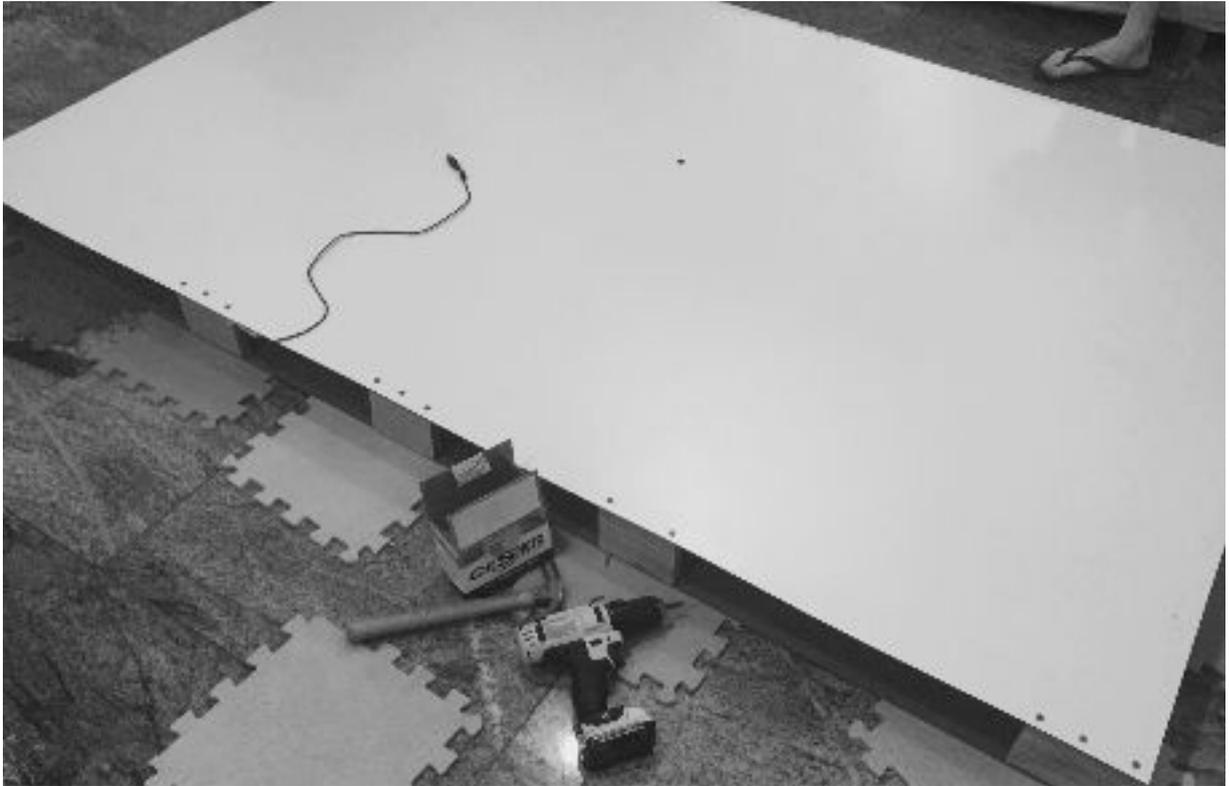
Tela sendo aparafusada. Face superior e cabo da câmera visíveis e em primeiro as ferramentas e caixa de parafuso utilizados.
